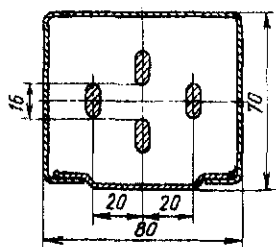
Поперечное сечение шинопровода ШРА4-100-44-1УЗ
